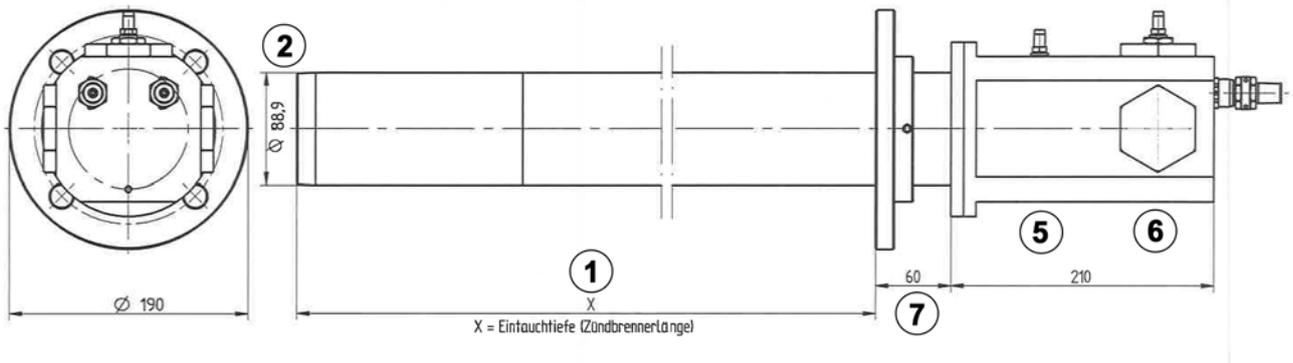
Abmessungen GF189 Zündbrenner Ausführung C
